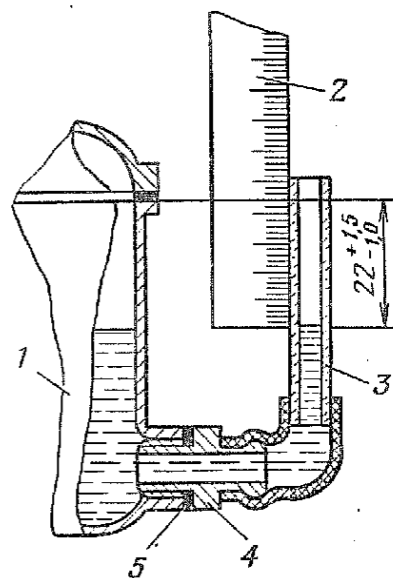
Проверка уровня топлива в поплавковой камере карбюратора:
